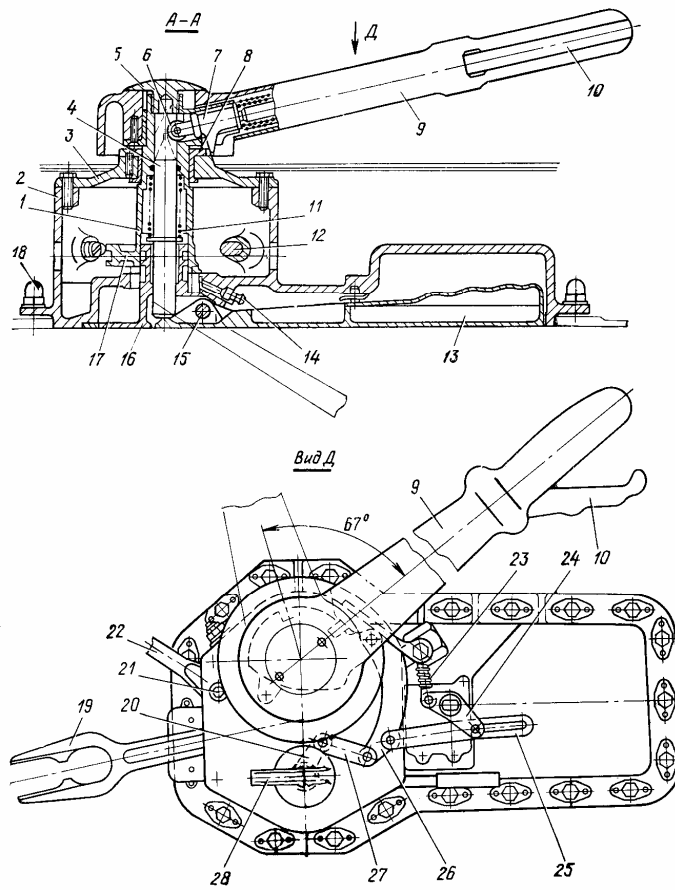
Механизм управления замками: 1—вал; 2—корпус; 3—крышка; 4—толкатель; 5—винт внутренней ручки; 6—ролик стопора; 7—стопор; 8—стопорная пластина; 9—внутренняя ручка; 10—гашетка; 11—пружина; 12—винт ограничитель; 13—наружная ручка; 14—масленка; 15—валик наружной ручки; 16—фланец; 17—рычаг вала; 18—герметическая гайка; 19—вилчатая тяга; 20—рычаг флажка; 21—масленка; 22—ведущая тяга; 23—фиксатор; 24, 26—рычаги; 25—тяга фиксатора; 27—серьга; 28—флажок
